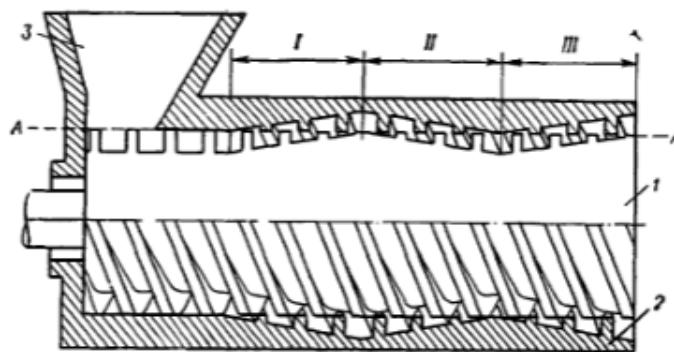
Схема змішувача зі змінною нарізкою шнека та корпусу: 1 - шнек; 2 - корпус; 3 - завантажувальна воронка; I-III - зони змішання; А-А - поверхня інтенсивних напружень зсуву
